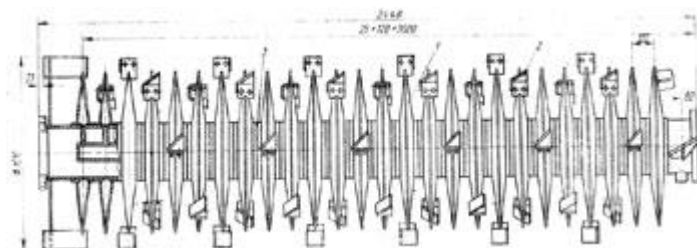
Сушилка окончательная: 1 - входное и выпускное отверстия для воздуха; 2 - воздушный клапан; 3 - разгрузочная камера сушилки; 4 - распределительная труба для подачи пара и удаления конденсата; 5 - конденсатоотводчик; 6 - лопасти; 7 - полые диски; 8 - ротор полый
